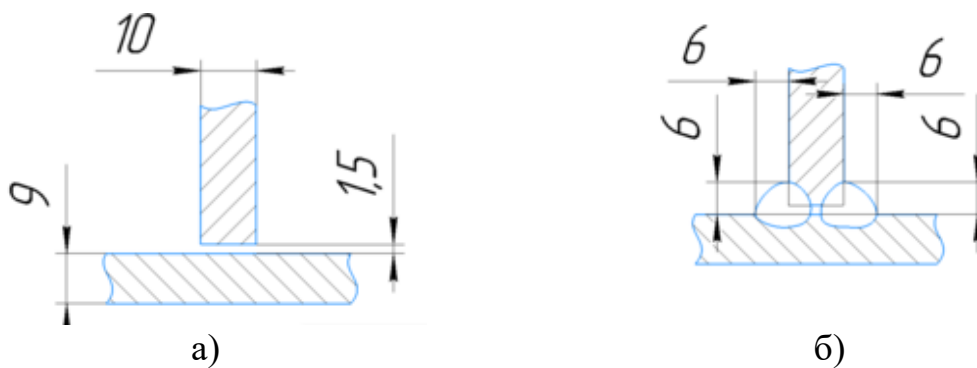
Сборка(а) и Сварка(б) соединения №1
